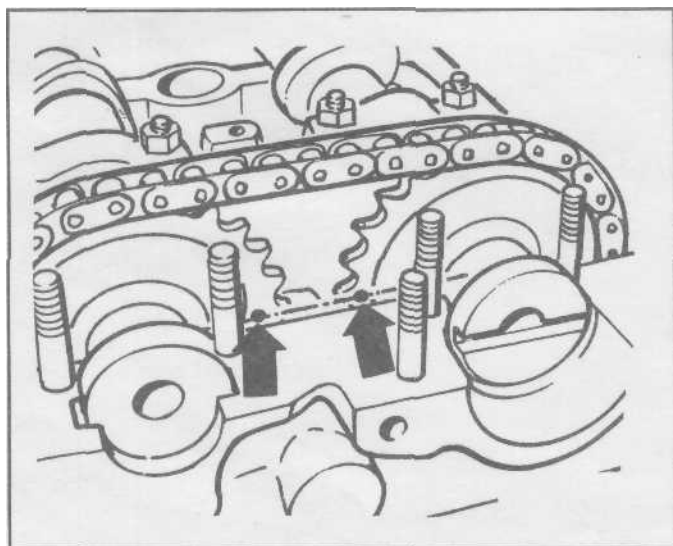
Регулировка натяжения ремня привода распределительного вала при помощи приспособления VW 210
